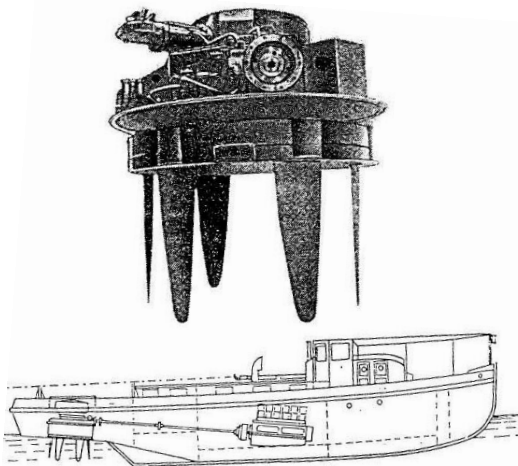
Крыльчатый движитель – общий вид и компоновка на катере
